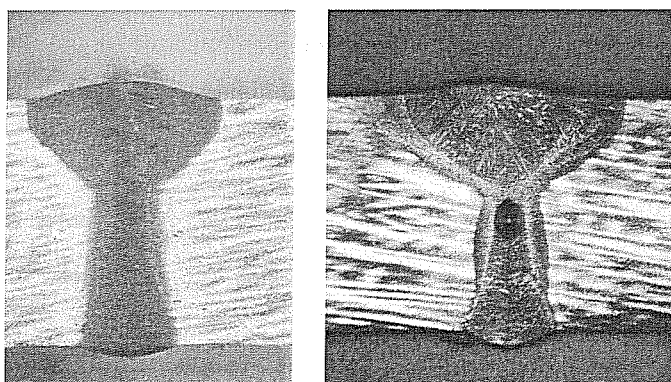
Macrografie su inconel 625, a sinistra solo LASER a destra LaTIG
